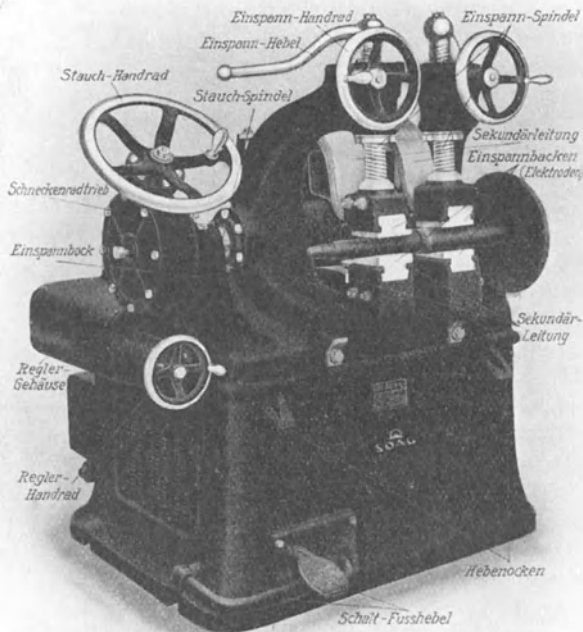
Größere Stumpfschweißmaschine.
